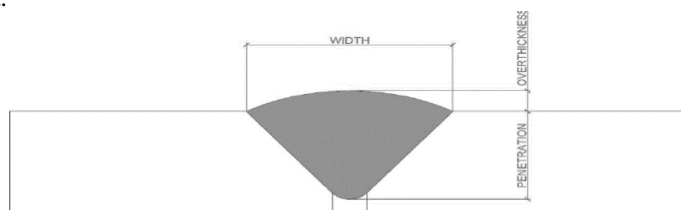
Geometría de un cordón de soldadura (vista transversal) (Siddharth Kumaran y Oliver Nesa Raj, 2018)
